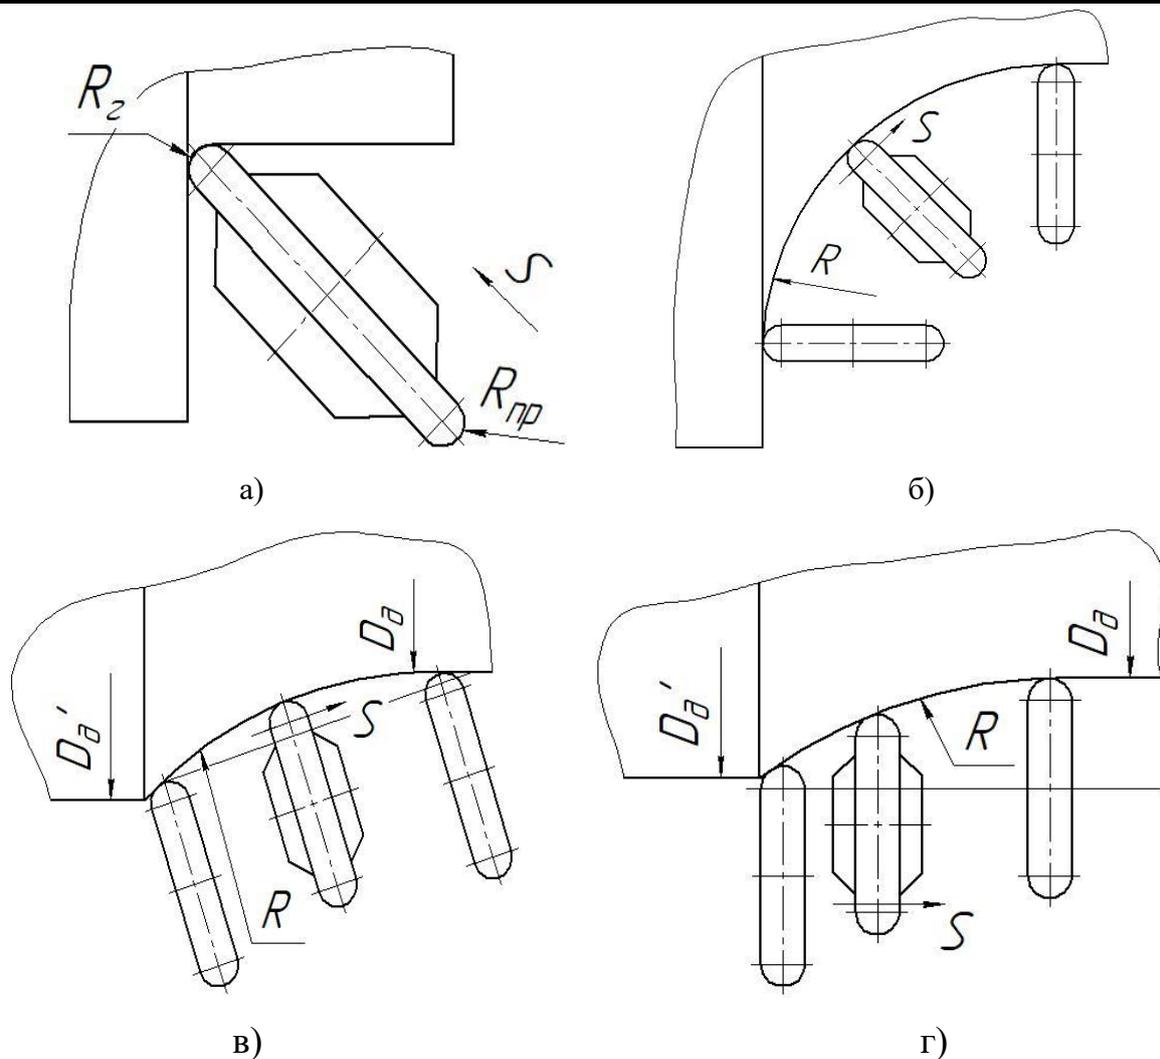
Схемы обкатывания переходных поверхностей:
